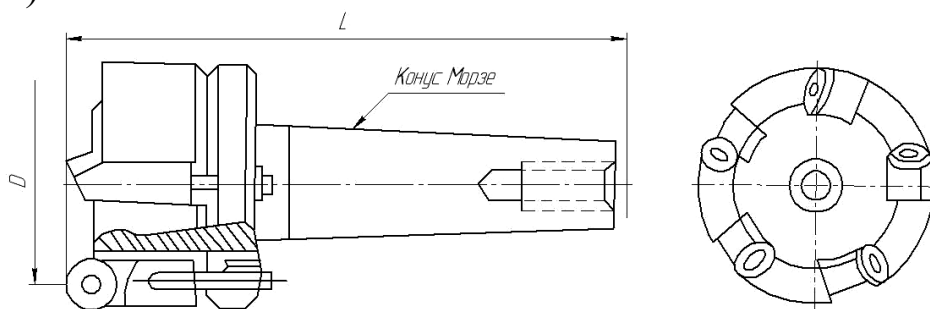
Фрезы торцовые: а) быстрорежущая насадка;
